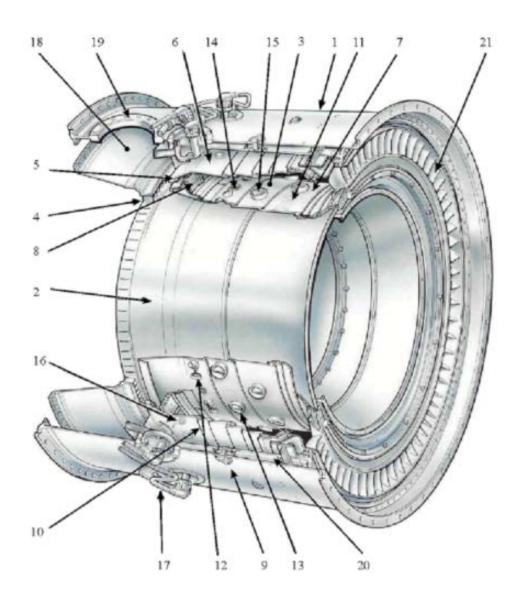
Кольцевая КС: *1* – наружный корпус; *2* – внутренний корпус; *3* – жаровая труба; *4* – направляющий аппарат компрессора; *5* – кольцо диффузора наружное; *6* – наружная стенка жаровой трубы; *7* – внутренняя стенка жаровой трубы; *8* – фронтовая плита; *9* – подвеска жаровой трубы; *10* – пояс системы охлаждения; *11* – отверстия перфорации; *12* – отверстия подвода воздуха в первичную зону; *13* – отверстия зоны смешения; *14* – козырек; *15* – втулка; *16* – топливная форсунка; *17* – топливный коллектор; *18* – полость отборов воздуха; *19* – фланец отбора воздуха; *20* – внутренняя стенка наружного корпуса; *21* – сопловой аппарат турбины
